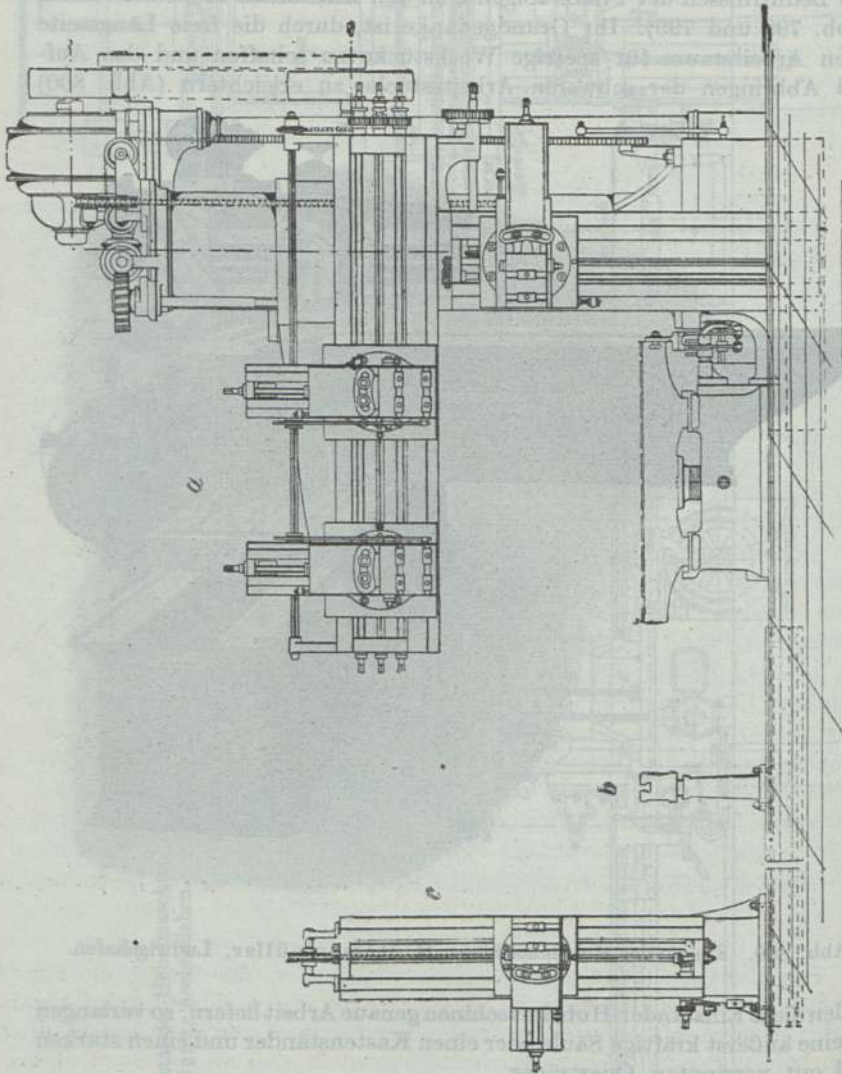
Einständer-Hobelmaschine mit 4 Hobelschlitten. Billeter & Klunz, Aschersleben.
